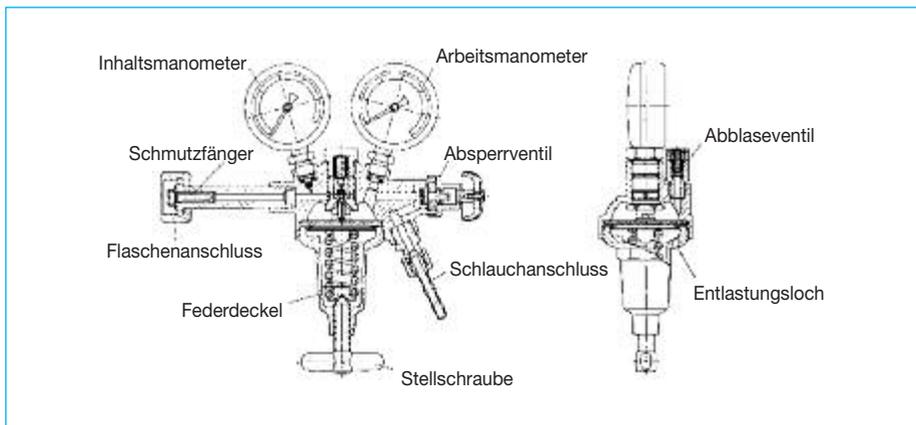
Acetylen-Flaschendruckminderer (Bauform für Deutschland: mit Anschlussbügel und Sicherheitsmanometern)
